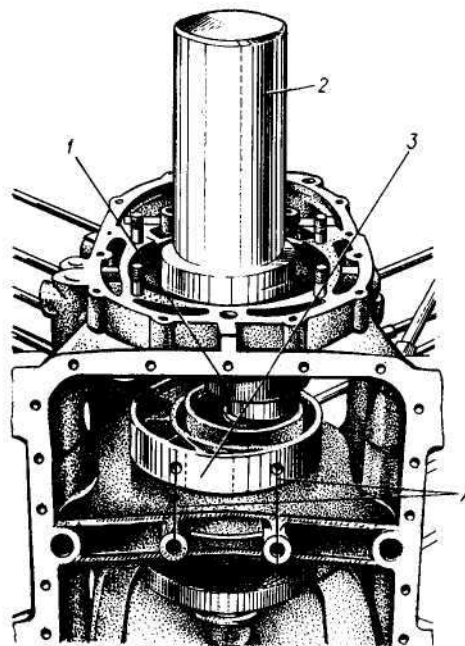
Запрессовка средней опоры в сборе с коленчатым валом в картер:
